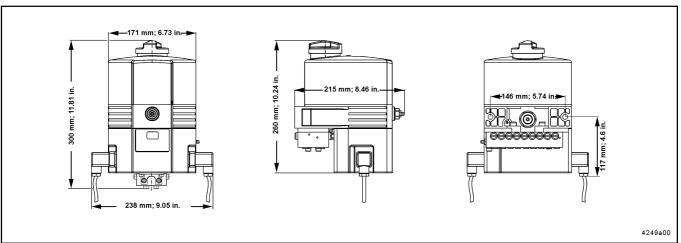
Cotes dimensionnelles de la pompe QLS 311
